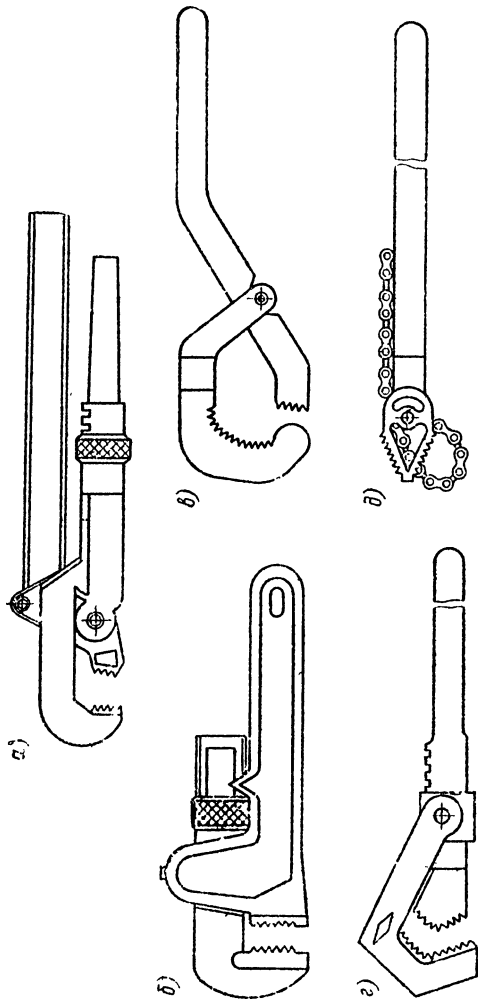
Ключи для сборки трубопроводов: а — рычажный; б — разводной, в — специальный; г — накладной; д — цепной
